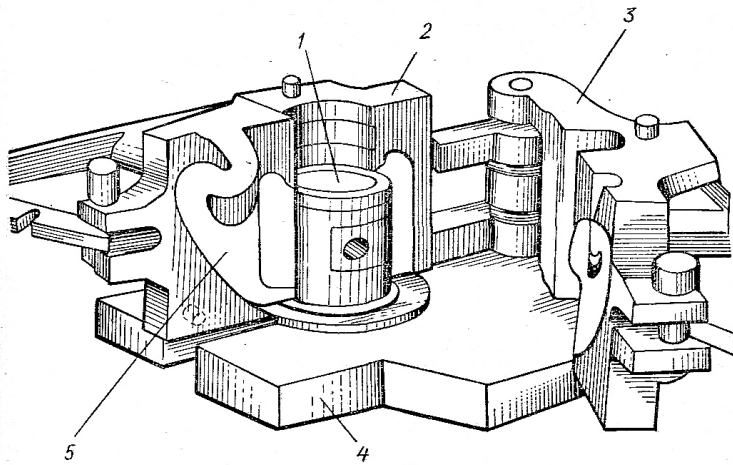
Металева форма для виготовлення поршня: 1 – заготівка (поршень); 2, 3, 4 – частини форми; 5 – ливникова система
